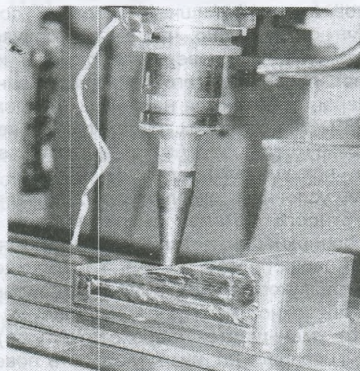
Фотография навесной оснастки с смонтированной в нее акустической системой, крепящейся в шпинделе фрезерного станка ГФ 2171
